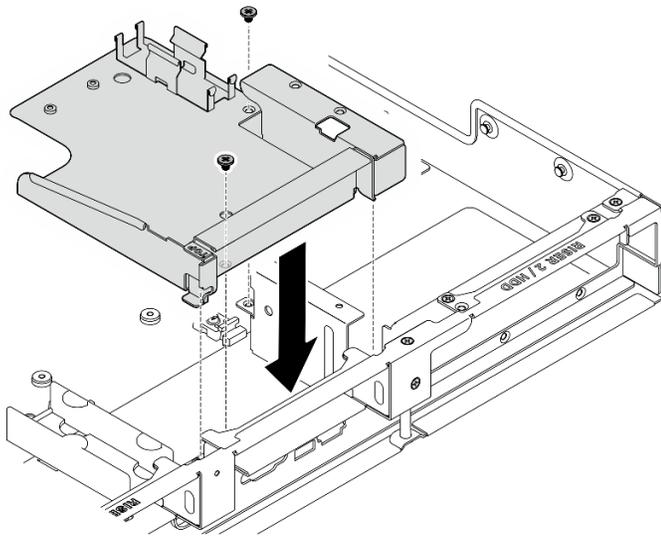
Instalando o suporte do módulo do sensor de vazamento
